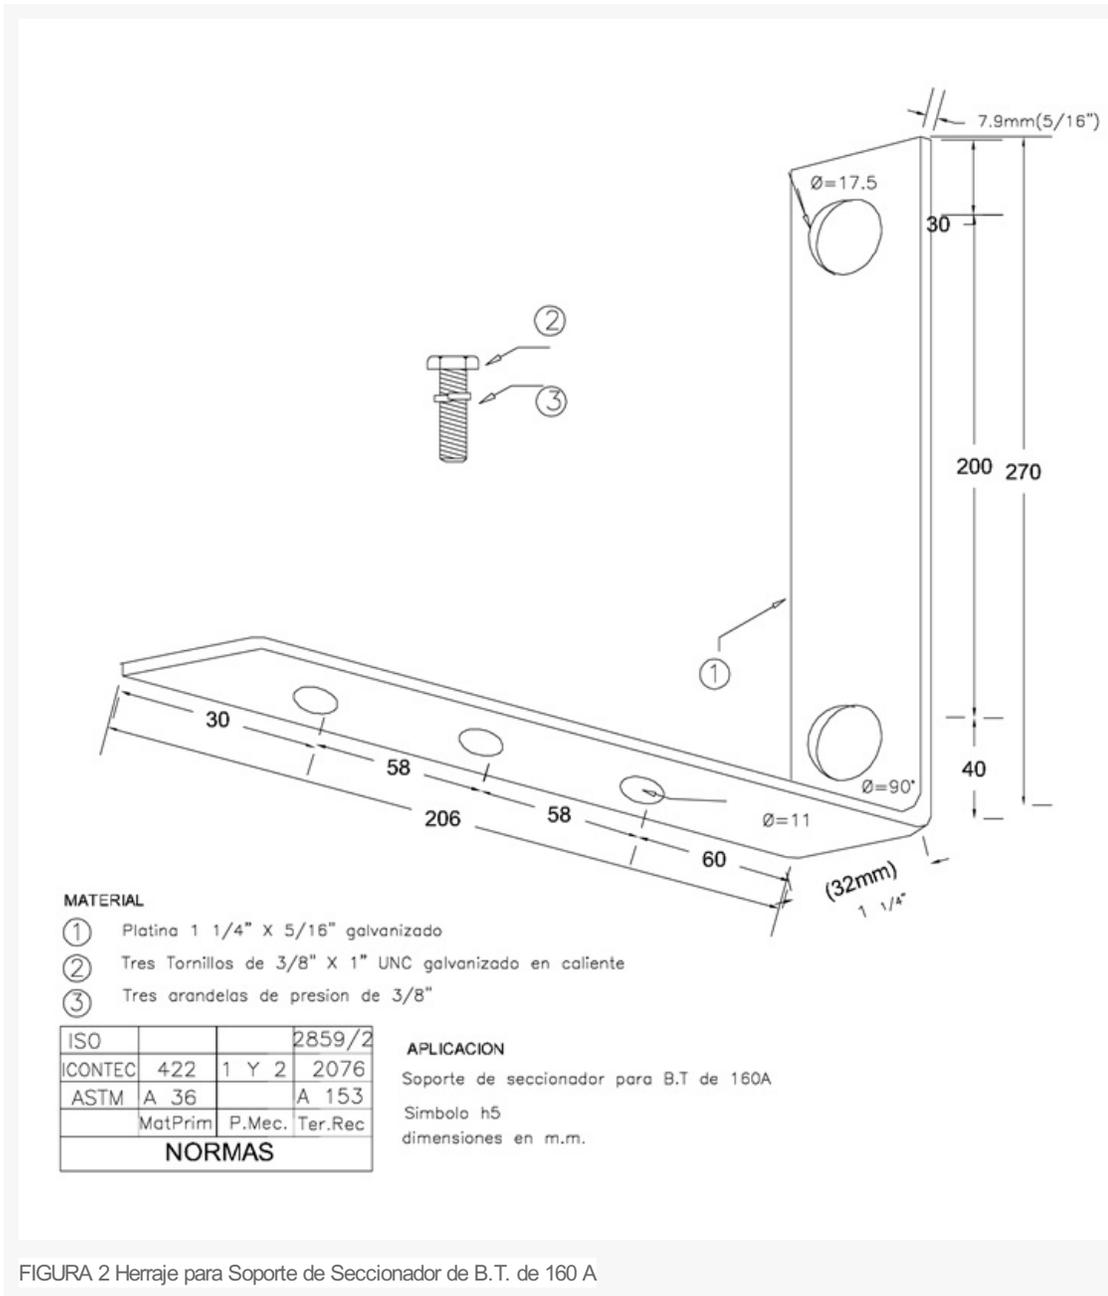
Herraje para Soporte de Seccionador de B.T. de 160 A
